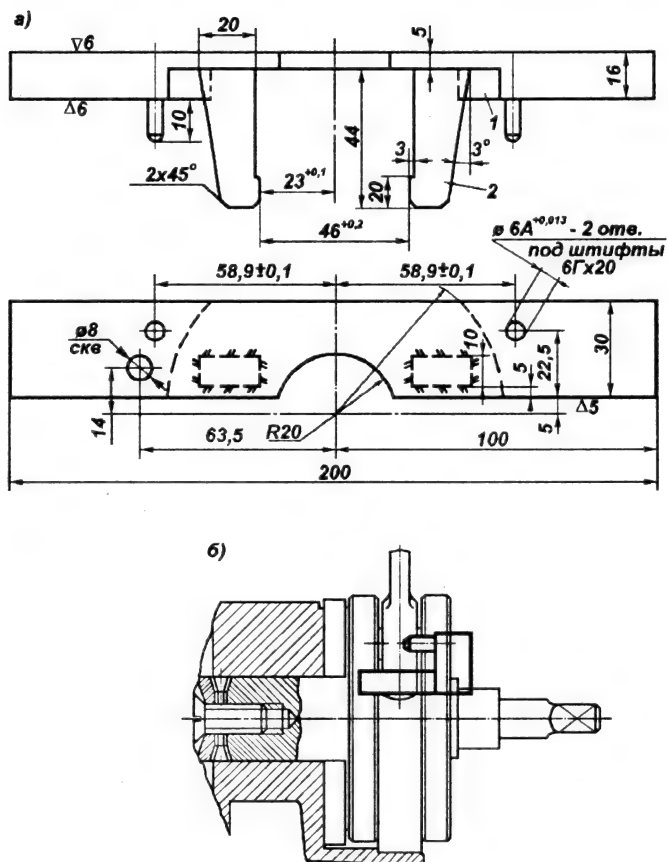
Упор для удержания коленвала при отворачивании и заворачивании стяжного болта (а) и установка упора на коленвал (б)
